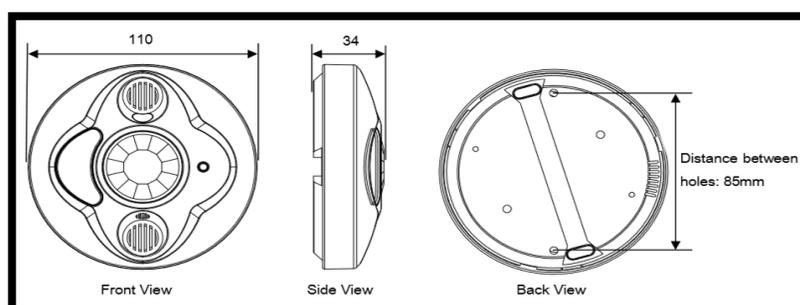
Dimensiones del sensor ultrasónico 12 en 1
